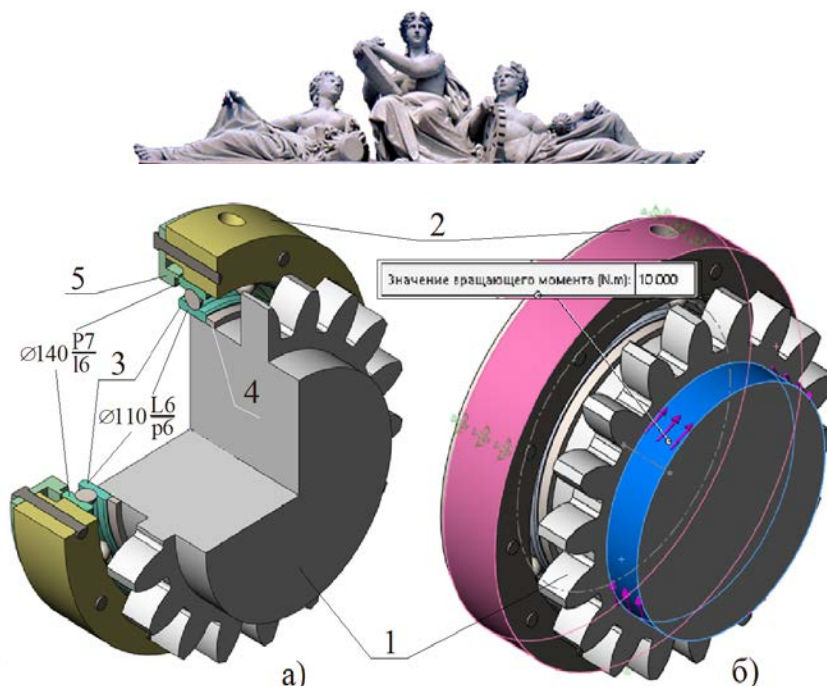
CAD модель механізму керування подачею сировини до засипного бункера
